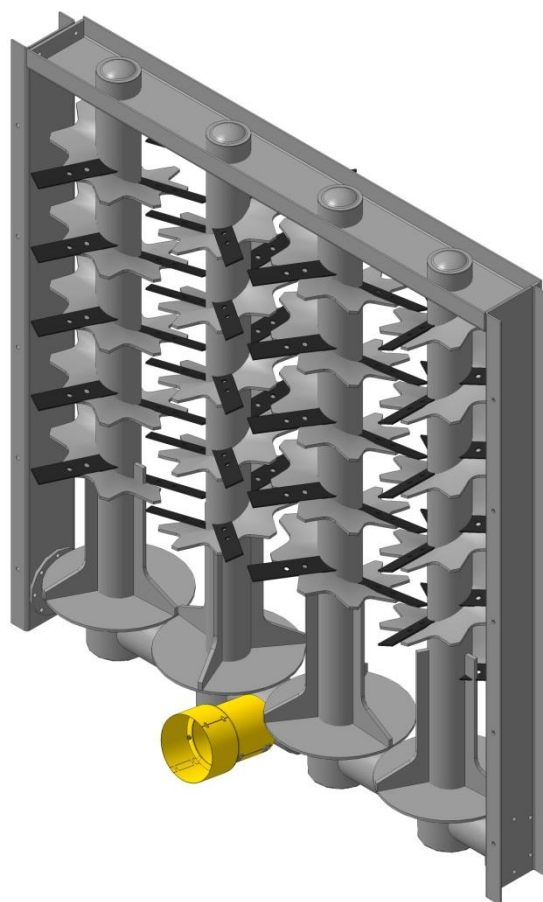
Разбрасыватель с четырьмя вертикальными барабанами
